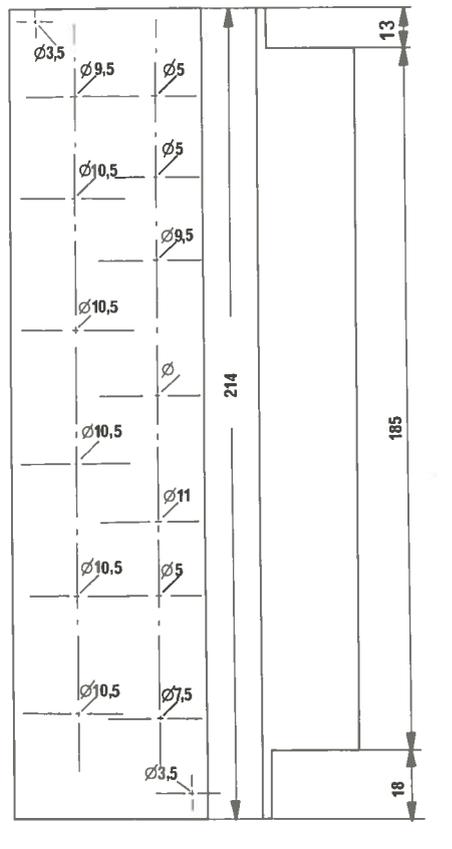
/16 - Procédure d'assemblage des cartes et face avant.
